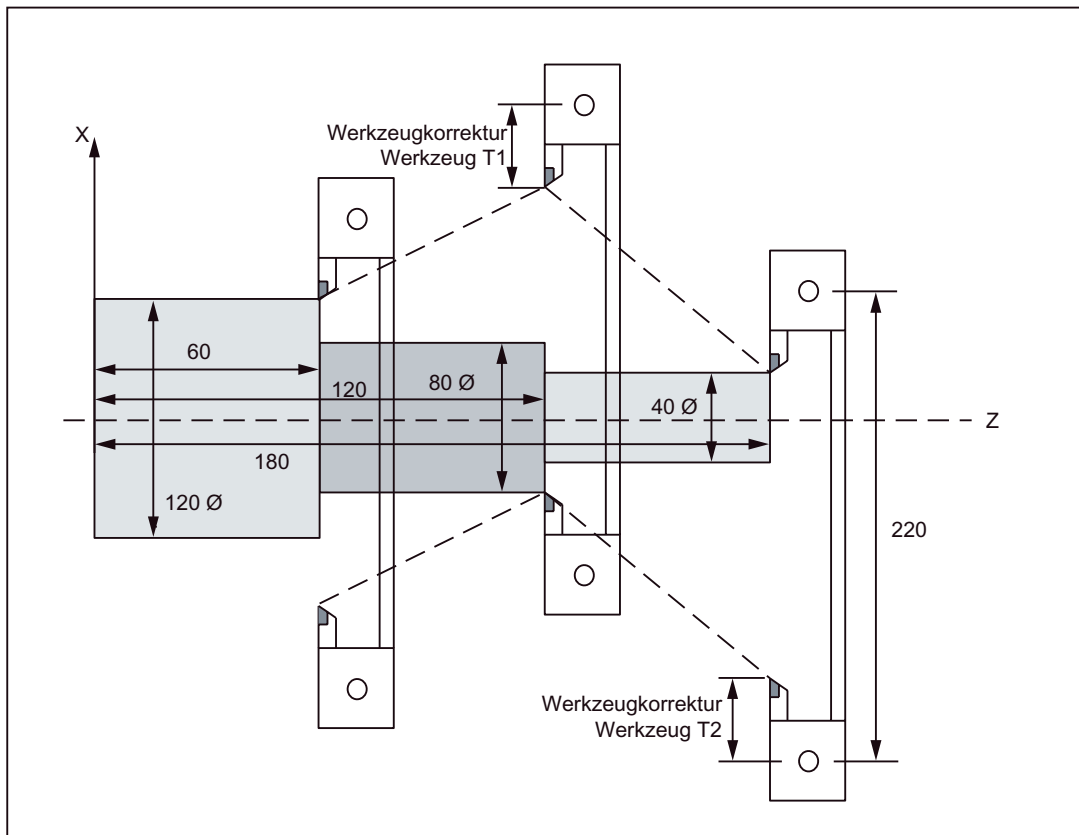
Bearbeitung mit 2 fest verbundenen Werkzeugen
